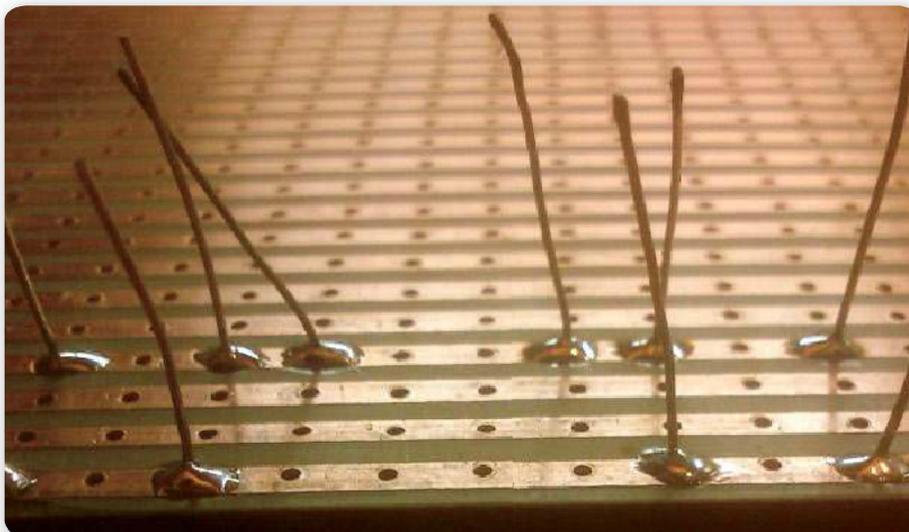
Limpiamos la punta del soldador y soldamos los componentes de una misma especie.
